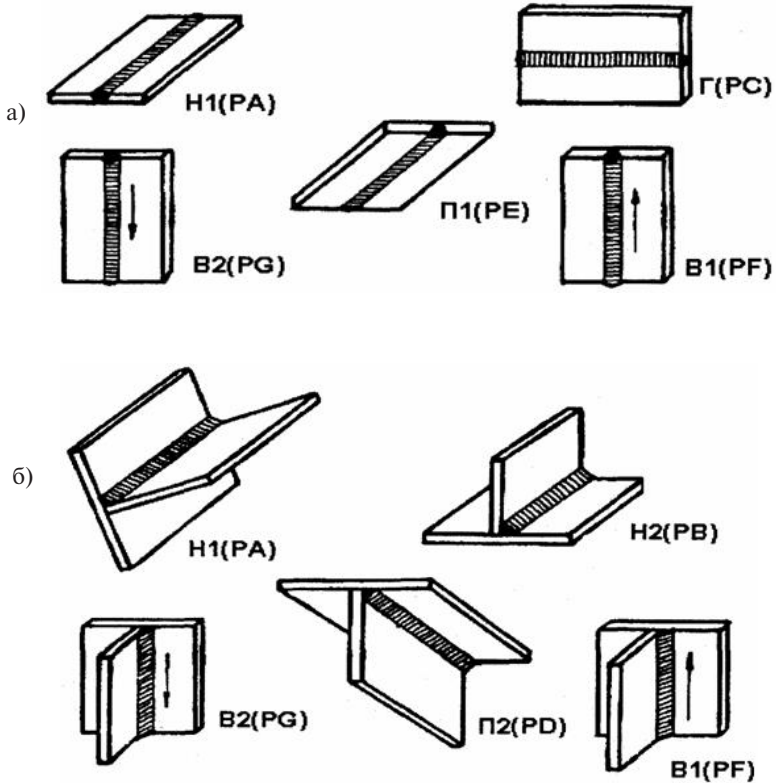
Положения при сварке стыковых (а) и тавровых (б) соединений листов: Н1 – нижнее; Г – горизонтальное; Н2 – нижнее тавровых соединений; В1 – вертикальное (сварка снизу вверх); В2 – вертикальное (сварка сверху вниз); П1 – потолочное; П2 – потолочное тавровых соединений
